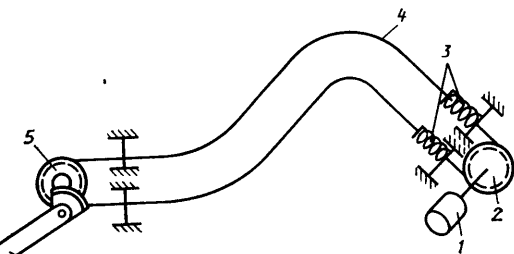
Конструкция привода с креплением оболочки тросов через пружины: 1 — электродвигатель постоянного тока; 2 — шкив; 3 — пружины; 4 — трос в оболочке; 5 — шкив и цепочка передач; 6 — палец
